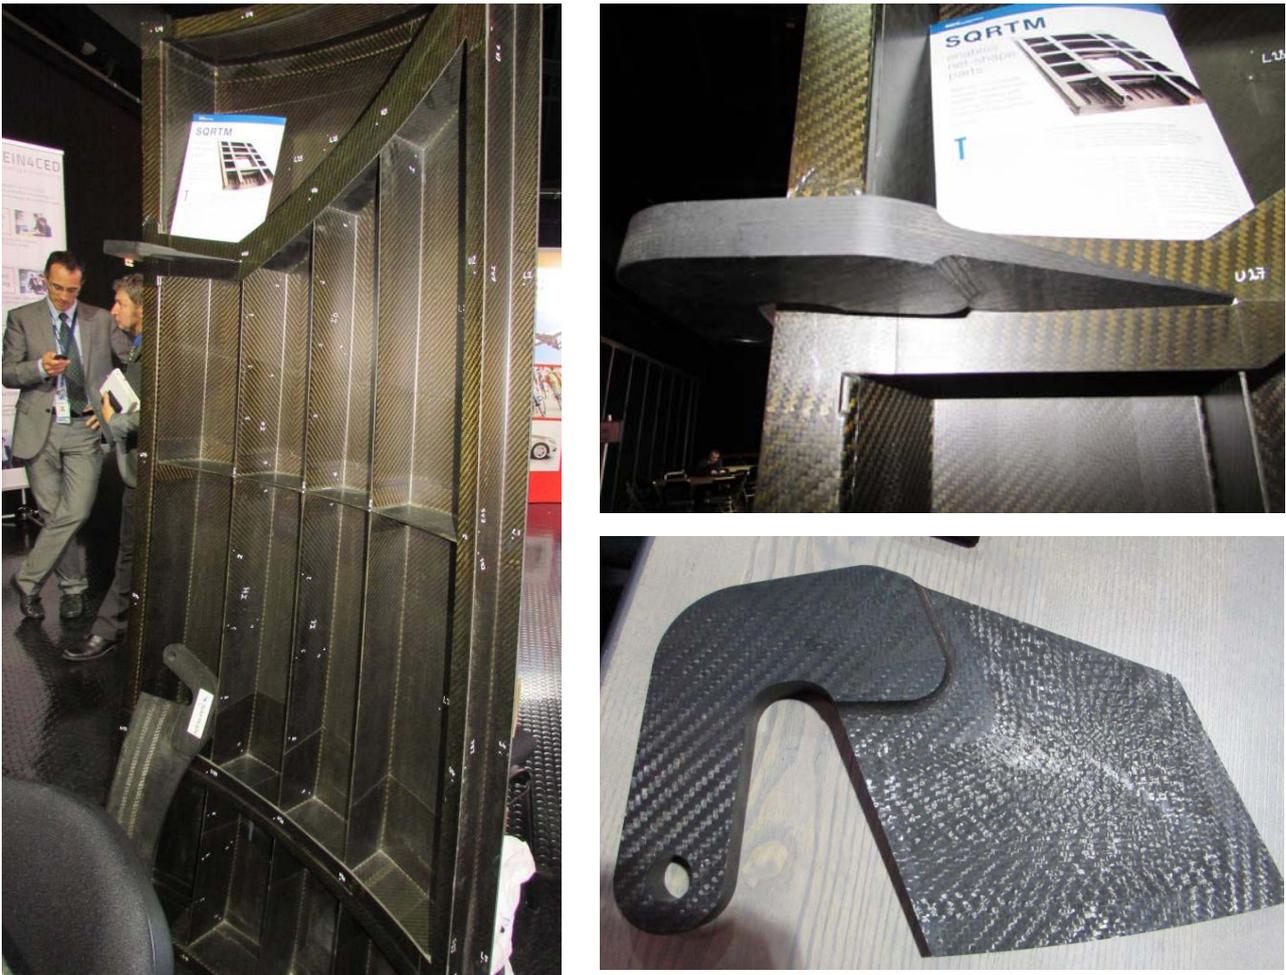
Фрагмент крыши вертолета из углепластика
